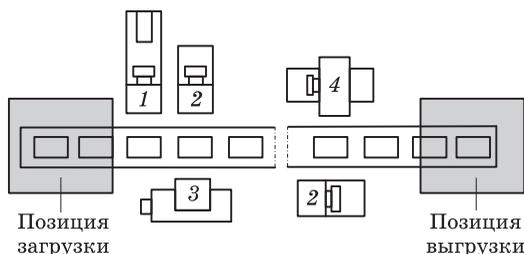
Однорядная линейная ГПС с отдельными позициями закрепления и открепления изделий (цифрами на рис. 1.13...1.16 обозначены номера рабочих мест)
